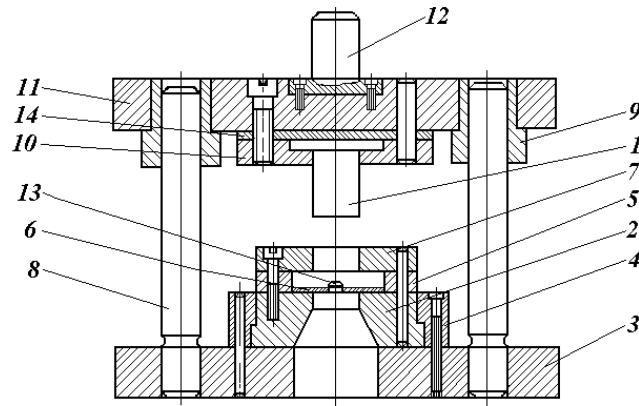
Штампу для виготовлення неметалевого одноразового абразивного інструменту
